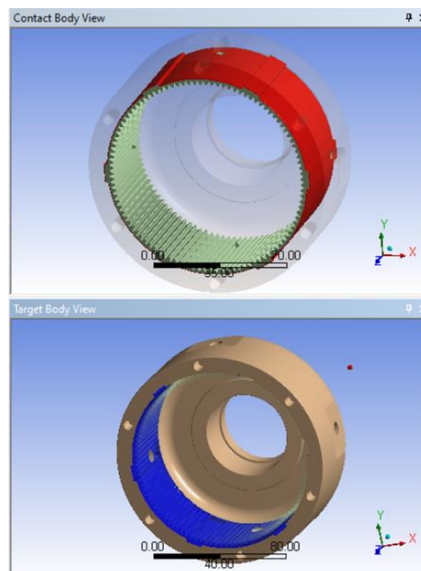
Faces de contacto Dentado *Ring Gear* e *Cloche
